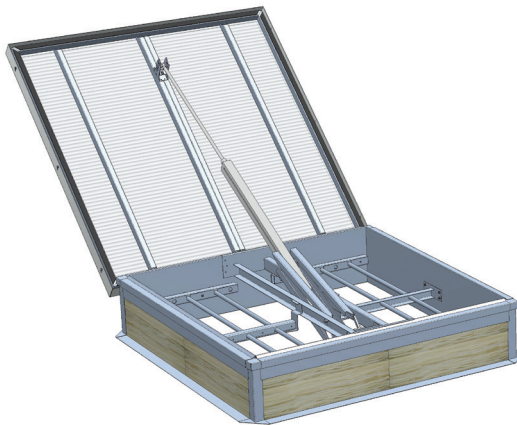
Przekrój klapy z zamontowaną kierownicą wlotową
